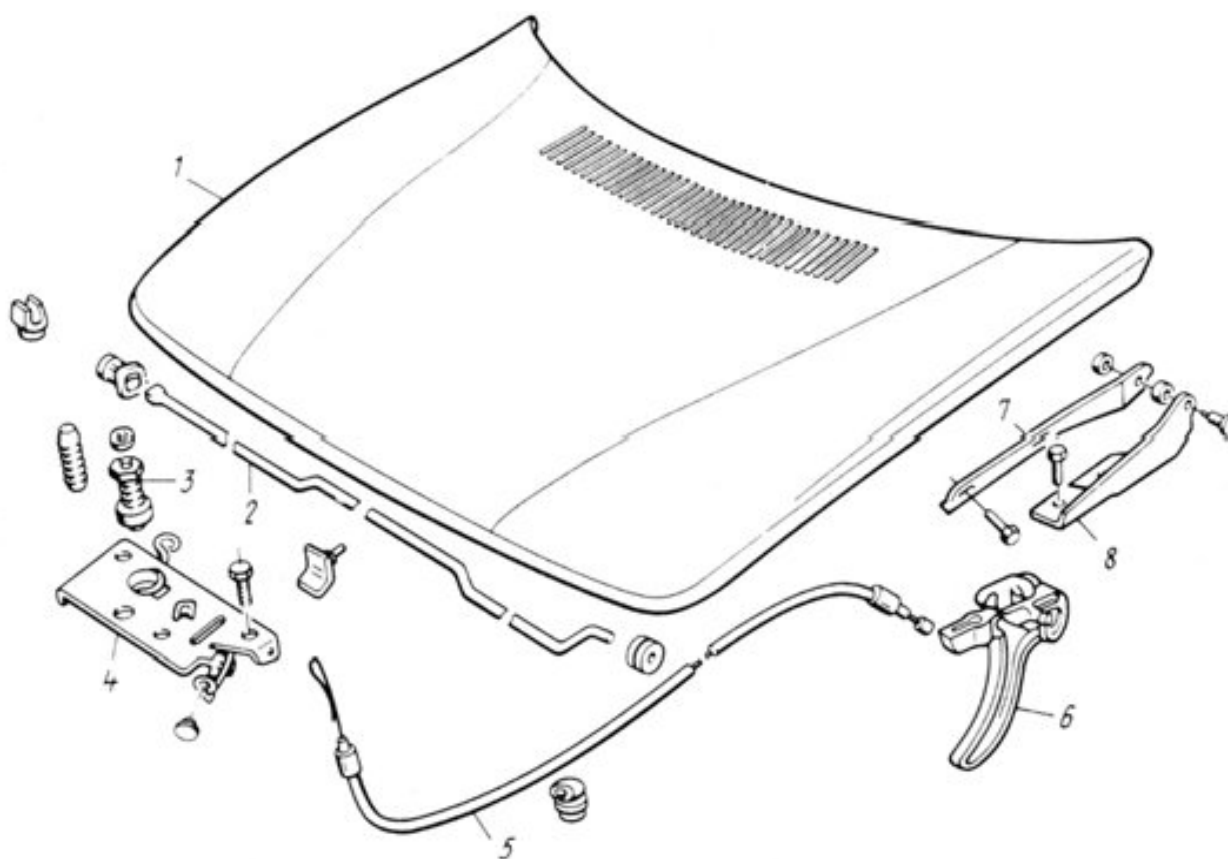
Капот двигателя автомобиля с механизмом открывания:
